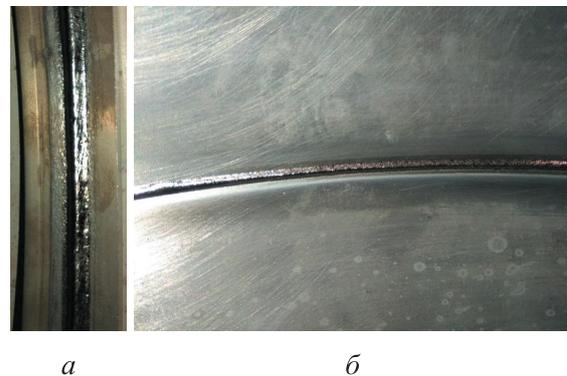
Внешний вид сварного шва (а) и внутренней поверхности сферы после удаления приспособления (б)
